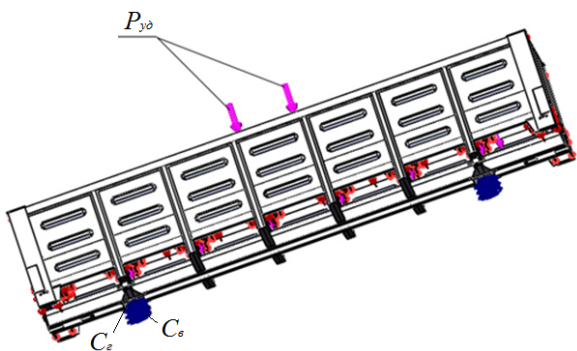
Розрахункова схема несучої конструкції напіввагона при розвантаженні грейферним ковшем (вид збоку)
